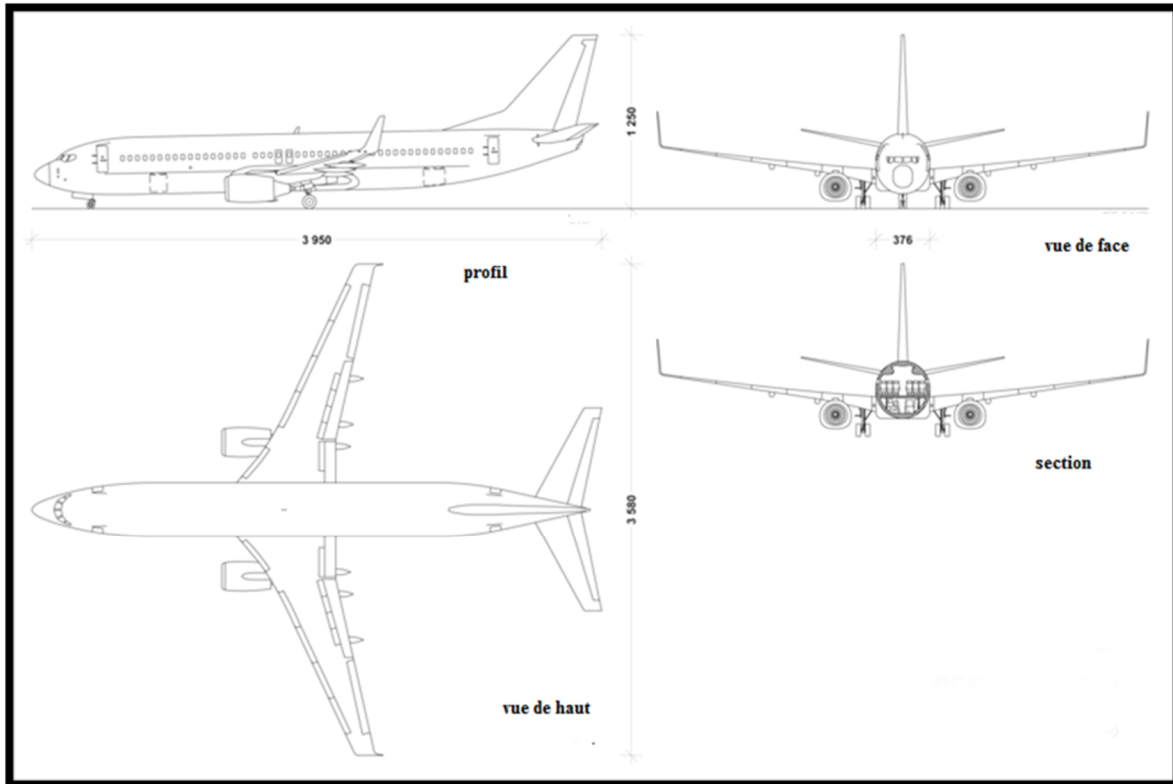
Planche architecturale du Boeing B737-800 NG
